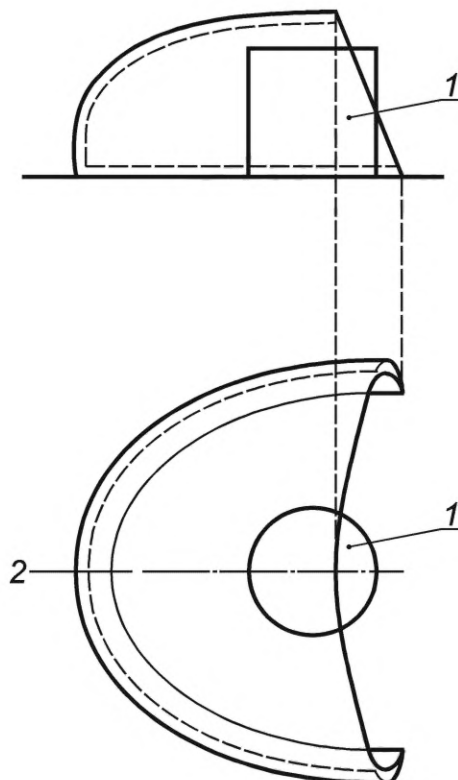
Пример подходящей конструкции зажимного устройства для неметаллических защитных носков
